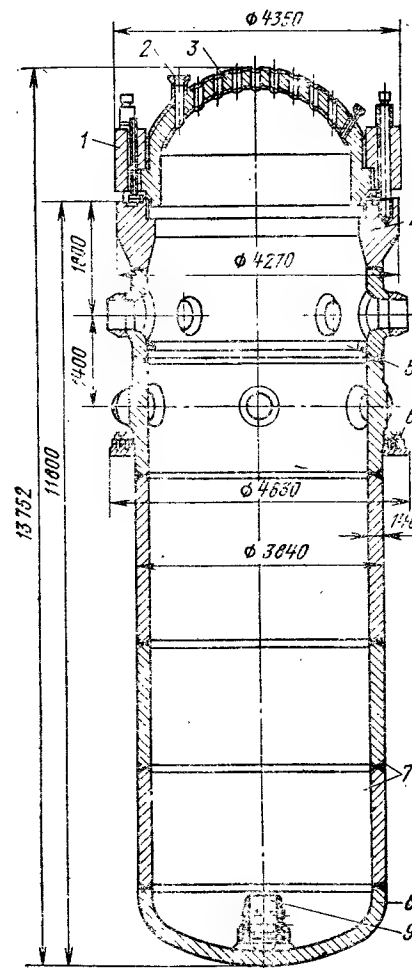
Корпус реактора ВВЭР-440 с крышкой:
